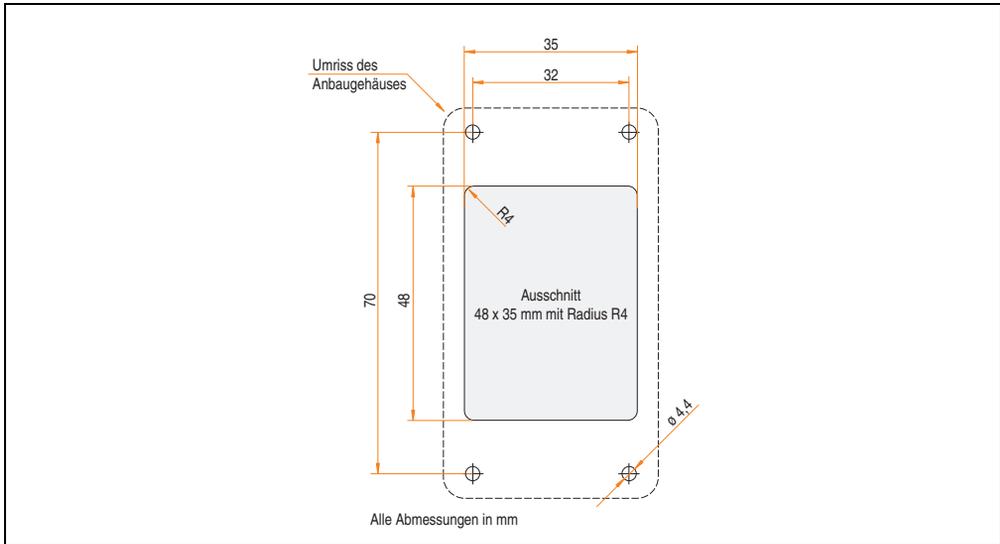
Bohrschablone für die Schaltschrankbuchse
